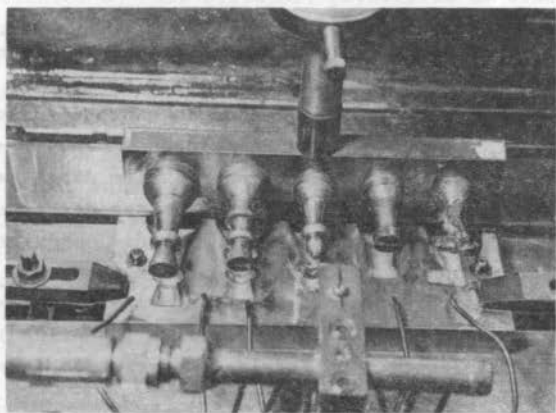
Dispositivo de montagem e fixação dos eletrodos-ferramenta e peça.
